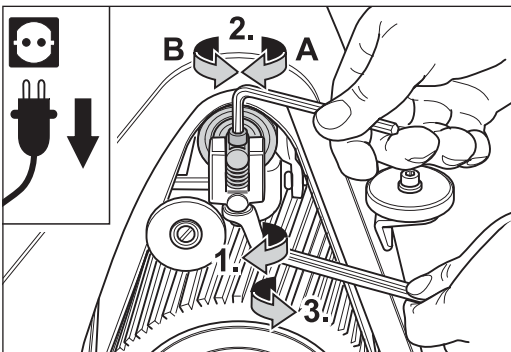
Justierung des Schleifbandlaufs an der Einstellschraube des Aggregats (siehe Haupttext).
